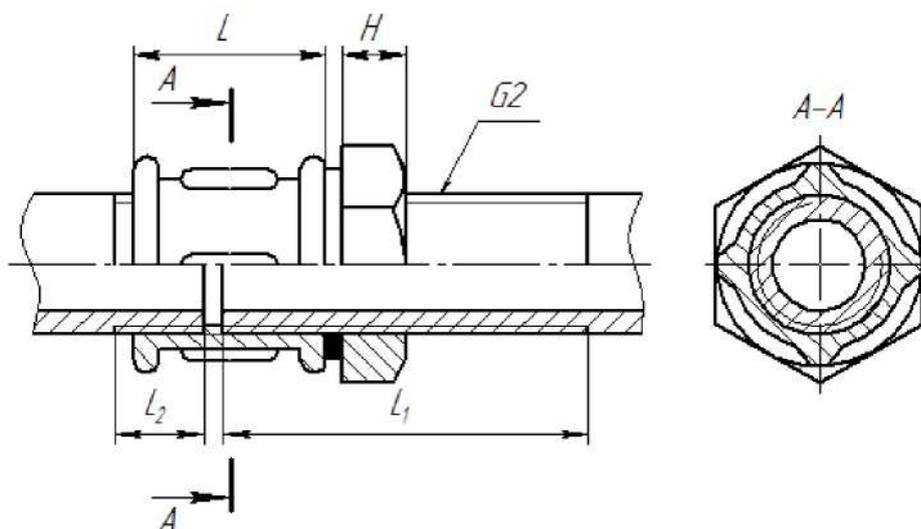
Чертеж соединения труб прямой короткой муфтой
